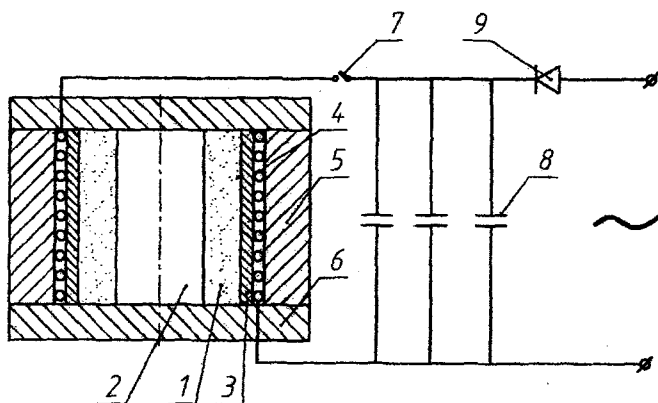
Схема устройства магнитно-импульсной штамповки порошковых втулок: 1 – засыпанная между оправкой 2 и втулкой 3 порошковая заготовка; 4 – индуктор; 5 – обойма; 6 – крышки; 7 – разрядник; 8 – конденсаторная батарея; 9 – выпрямитель электрического тока
